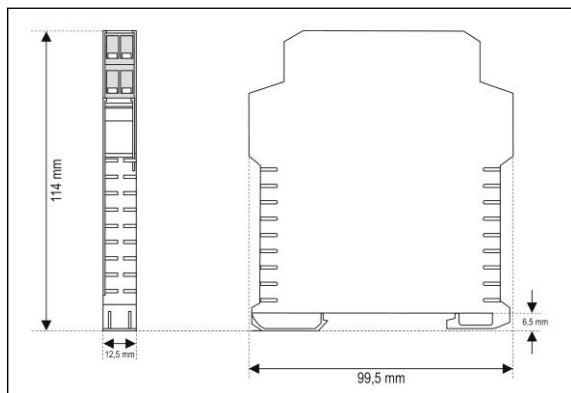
Dimensões do transmissor TxIsoRail-HART
